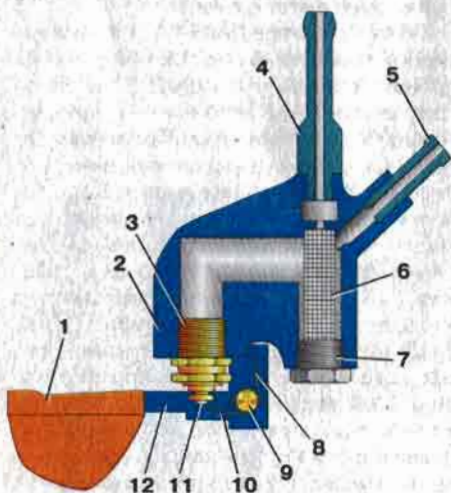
Схема поплавкового механизма и топливоприемной системы карбюратора: 1 - поплавки; 2 - крышка карбюратора; 3 - топливный клапан; 4 - штуцер подачи топлива; 5 - штуцер слива топлива в бак; 6 - топливный фильтр; 7 - пробка; 8 - ограничитель хода поплавка; 9 - ось поплавков; 10 - язычок кронштейна; 11 - запорная игла топливного клапана; 12 - кронштейн поплавков
